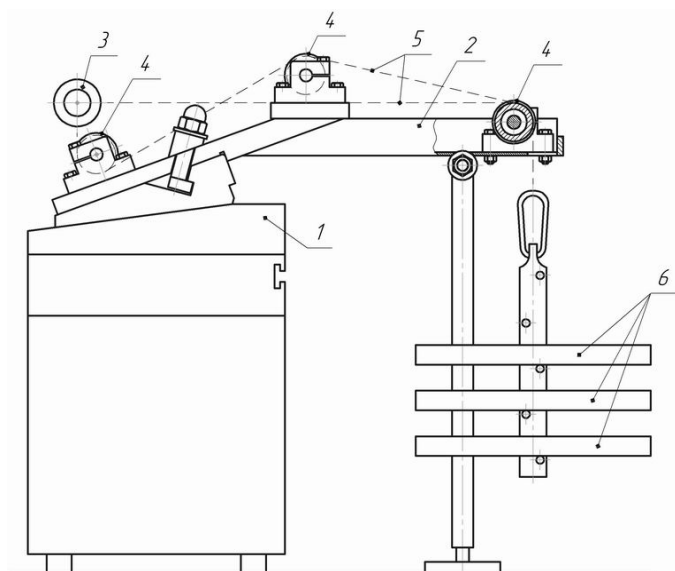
Приспособление для тарировки силоизмерительного устройства
